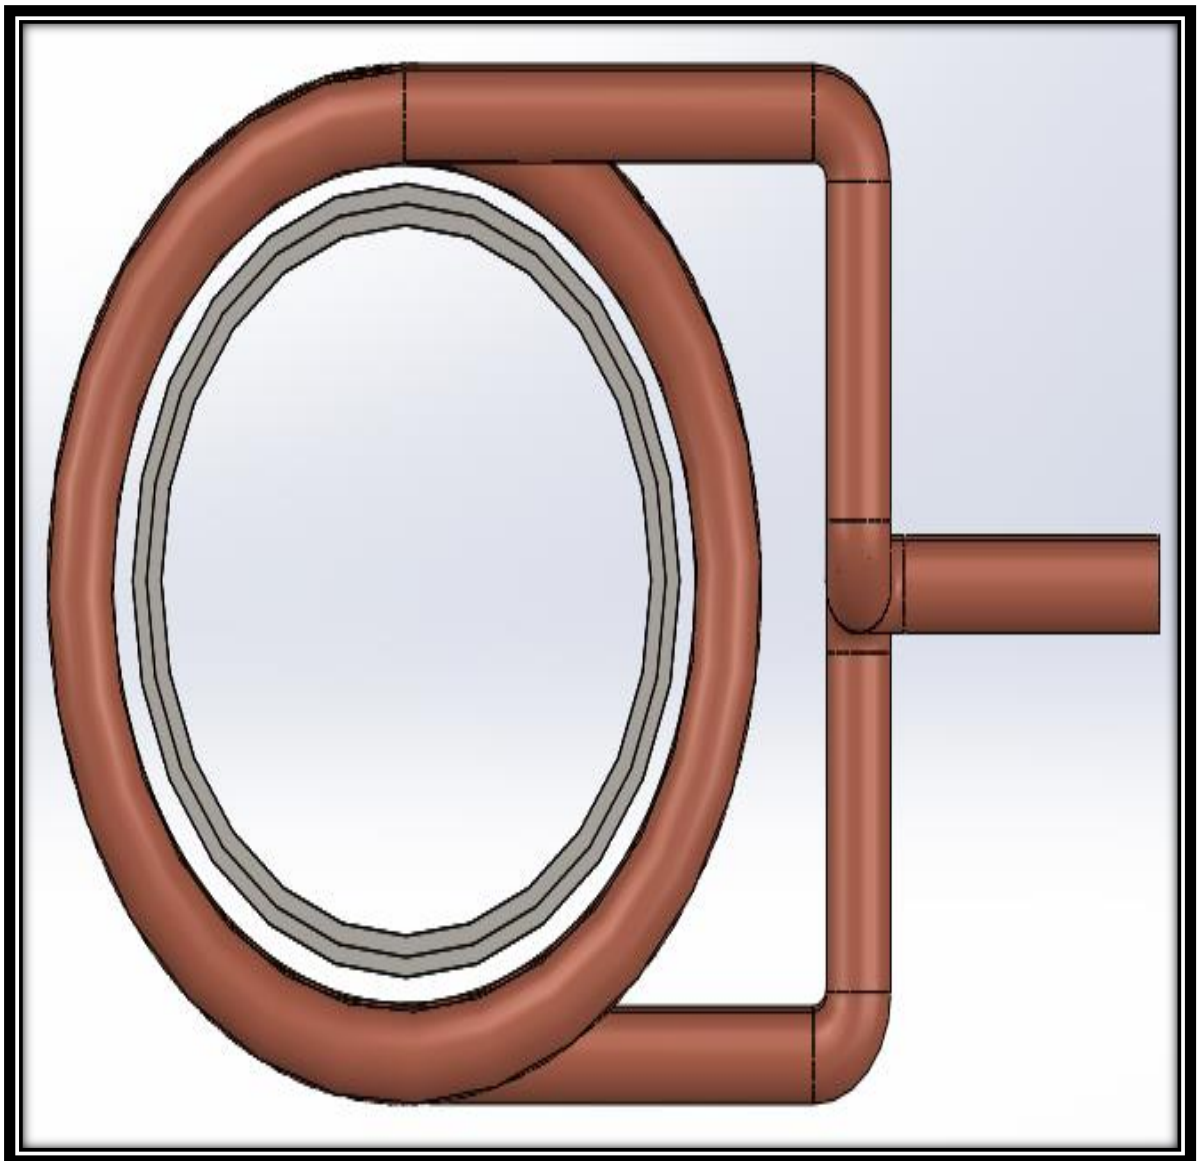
Ensamblaje de las Piezas 3D "Vista Superior"
